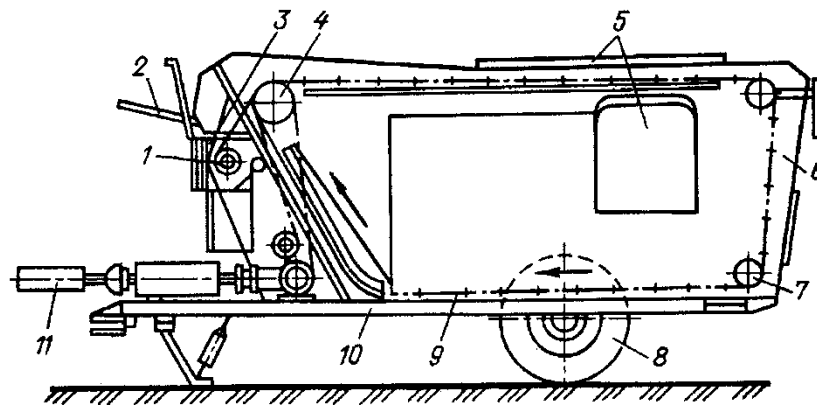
Схема кормороздавача КУТ-3,0А: 1-розвантажувальний шнек; 2-важіль повороту заслінки; 3-вивантажувальний пристрій; 4-приводні зірочки; 5-завантажувальні вікна; 6-бункер; 7-зірочки; 8-ходова частина; 9- ланцюгово-планковий транспортер; 10-рама; 11-вал відбору потужності.
